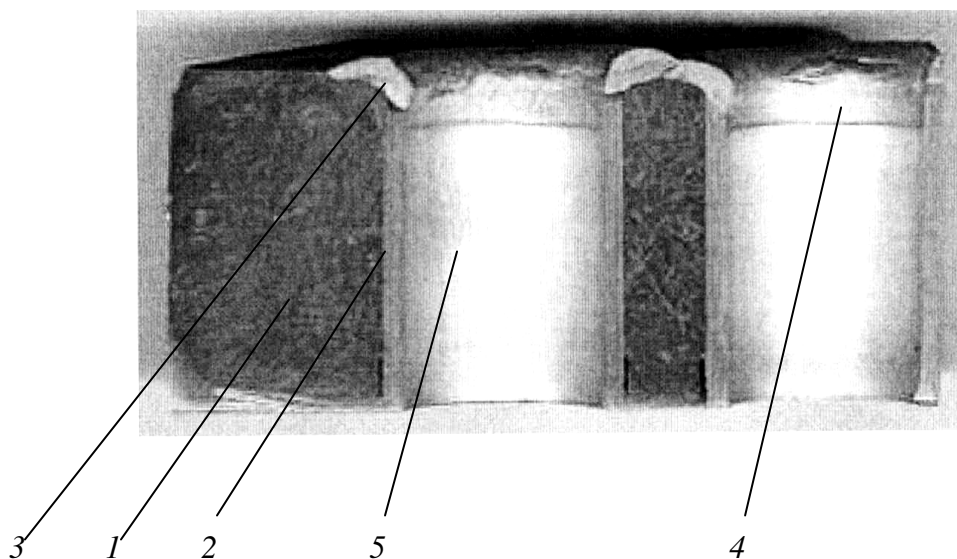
Продольный разрез узла крепления трубы. 1- доска; 2- труба; 3- сварной шов; 4- зона подвальцовки; 5 вальцованный участок
